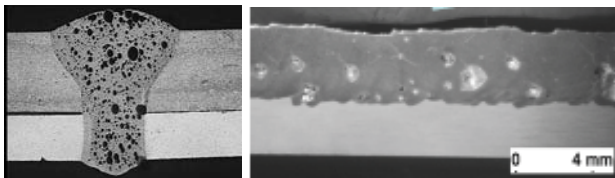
Charakteristische Schweißnahtfehler in Aluminium bzw. Aluminium-Druckguss: a) durch zwangsgelöste Gase hervorgerufene Poren; b) Prozessporen
